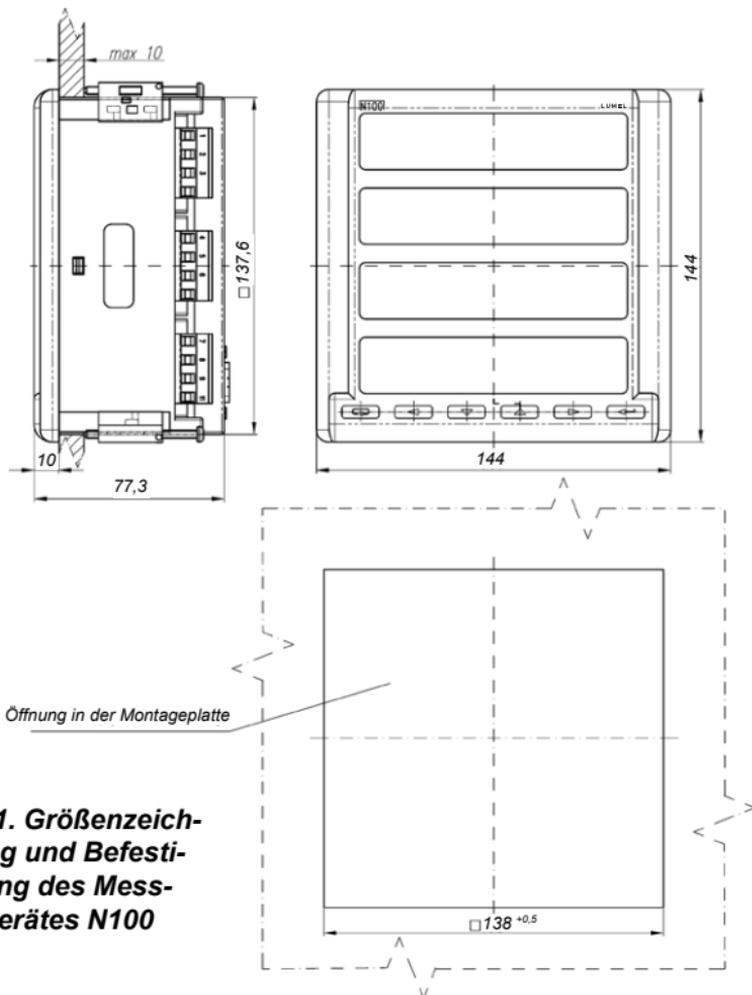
Größenzeichnung und Befestigung des Messgerätes N100
